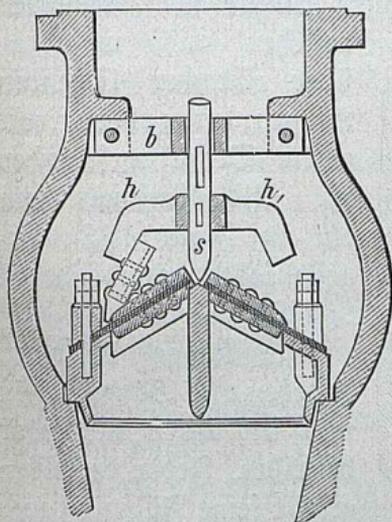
Dachförmiges Ventil mit zwei Klappen.
